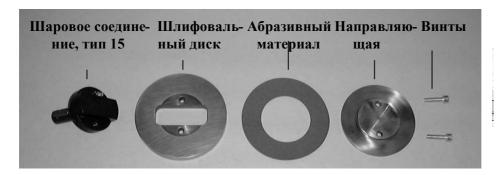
Компоненты инструмента для работы в режиме "ручного станка" с шаровым соединением типа 15 (твердые шлифовальные диски с направляющими)
